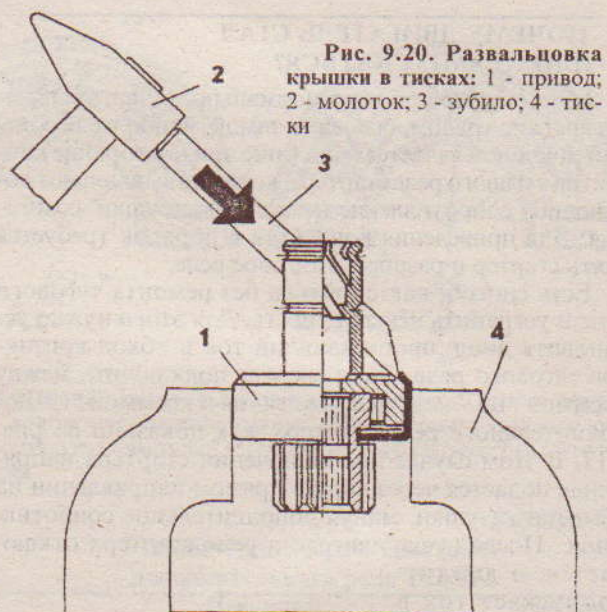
Развальцовка крышки в тисках: 1 - привод; 2 - молоток; 3 - зубило; 4 - тиски
